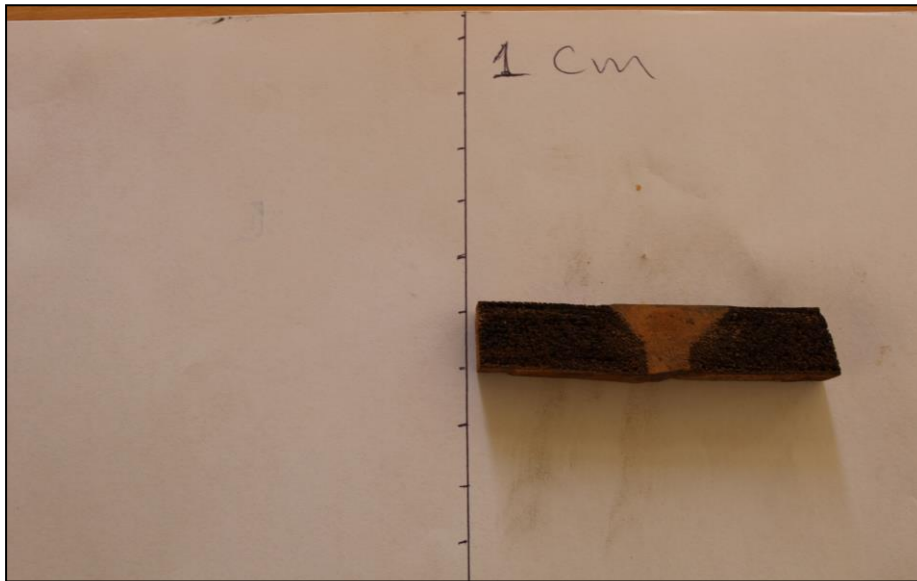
Aspect macroscopique de produits de corrosion en milieu HCl 1M
